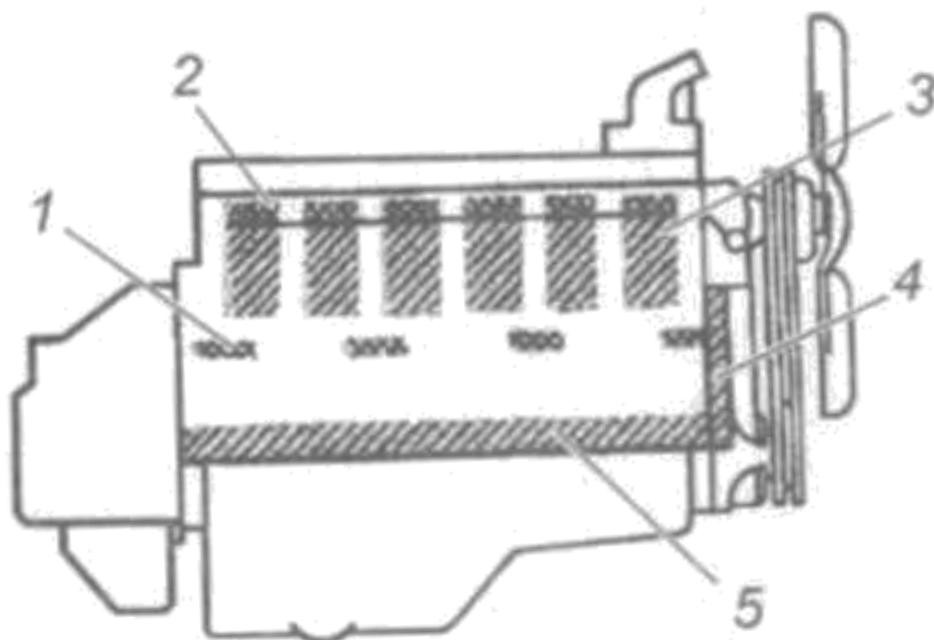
Зоны прослушивания двигателя для определения дефектов различных деталей: 1 – клапанов; 2 – поршневых пальцев, шатунных подшипников; 3 – Распределительных зубчатых колес; 4 – коренных подшипников; 5 – подшипников распределительного вала.
